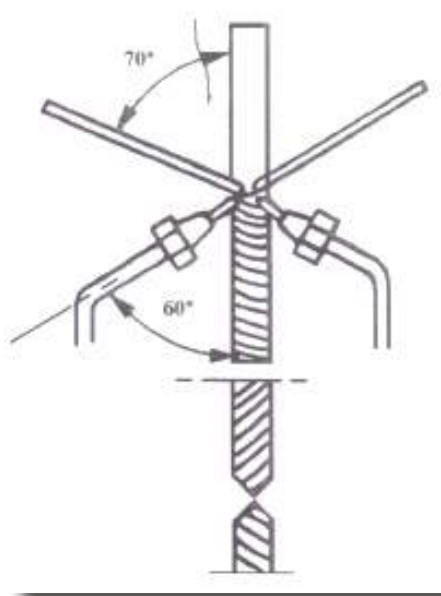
Soldadura ascendente com dois soldadores.
